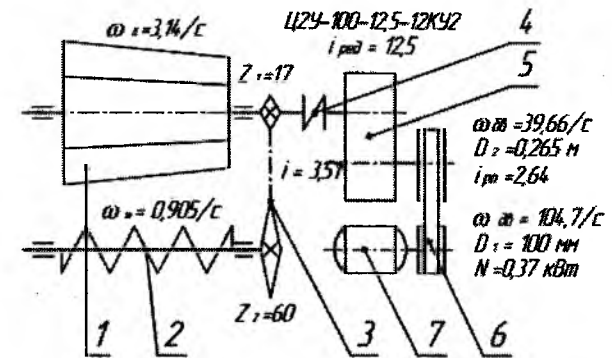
Кинематическая схема пирамидального бурата: 1- пирамидальный барабан; 2 - распределительный шнек; 3 - цепная передача; 4 - муфта; 5 - редуктор; 6 - ременная передача; 7 - электродвигатель
